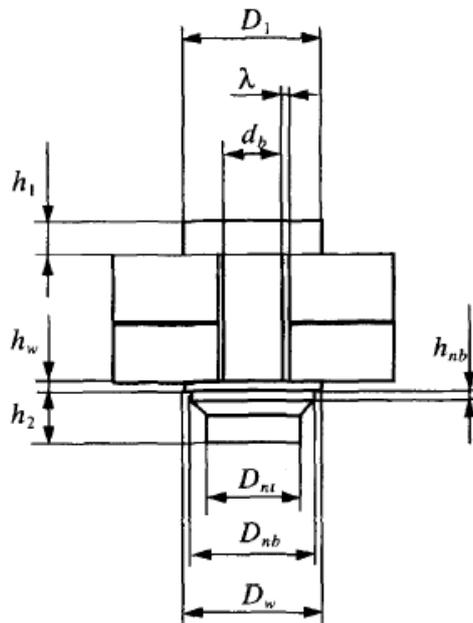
Dimensiones del tornillo de cabeza recta.
